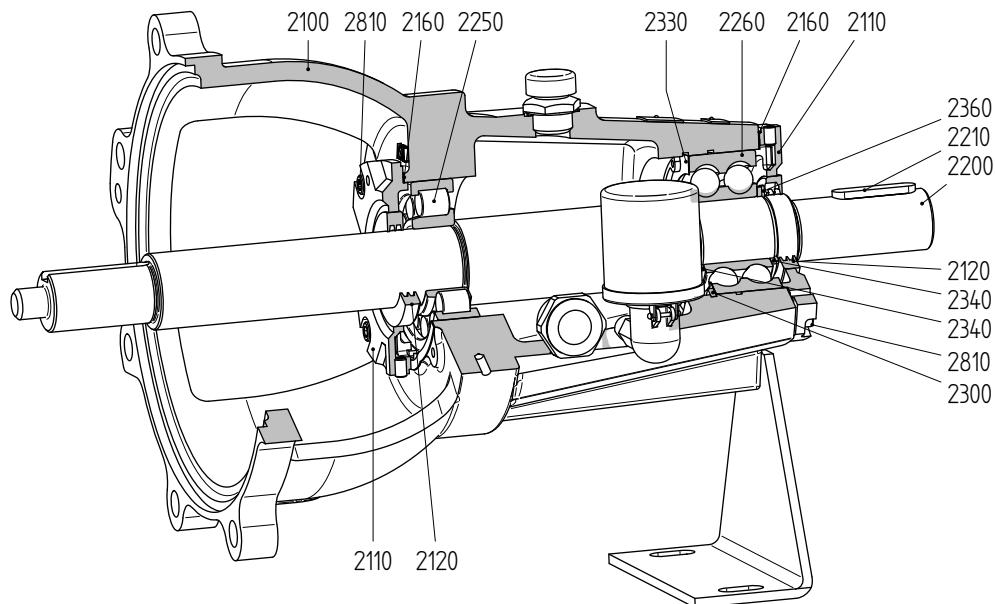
Подшипник L4 (усиленный, с масляной смазкой)
